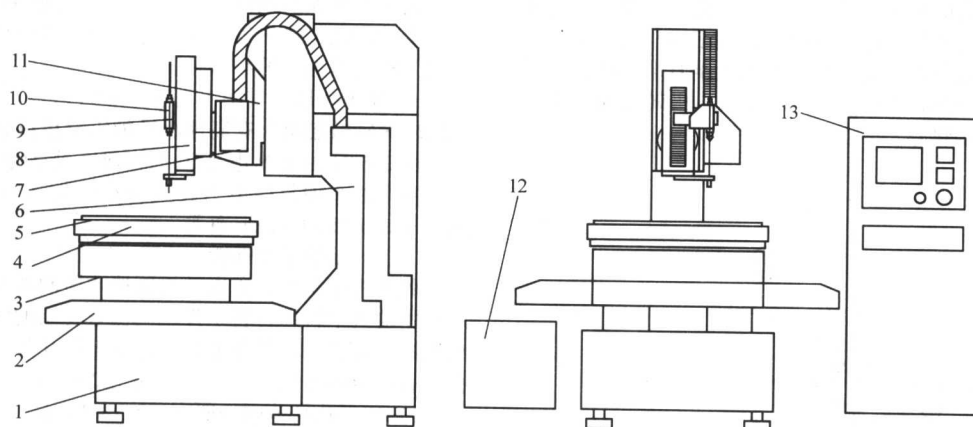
8 轴数控电火花高速小孔加工机床外形图
